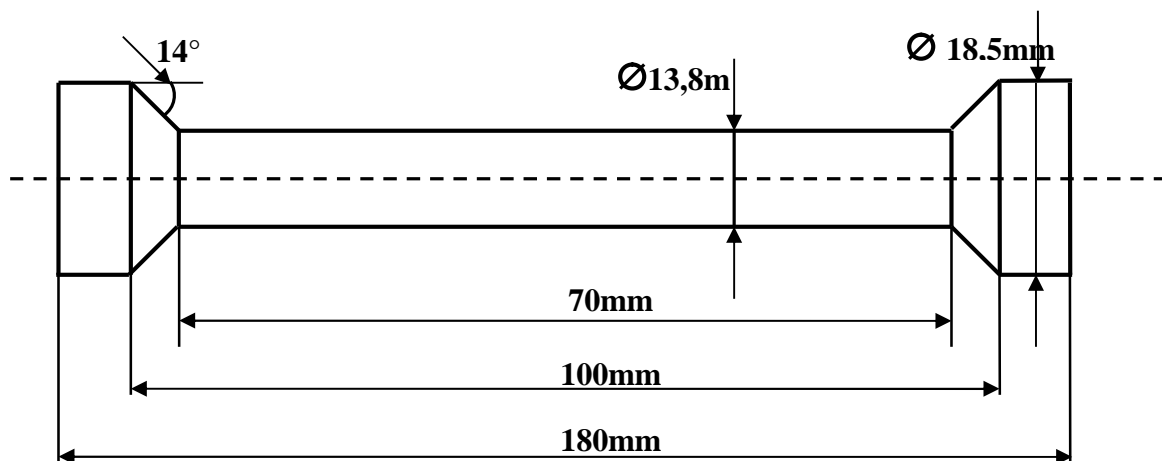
Formes et dimensions des éprouvettes de traction coulées en sable
